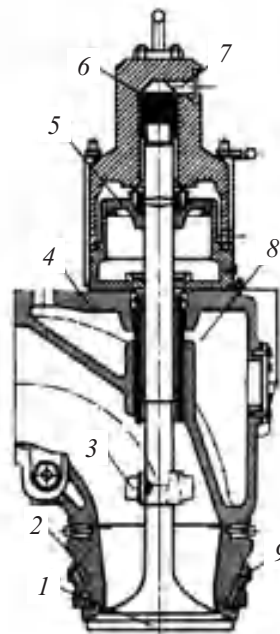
Випускний клапан з гідравлічним приводом
